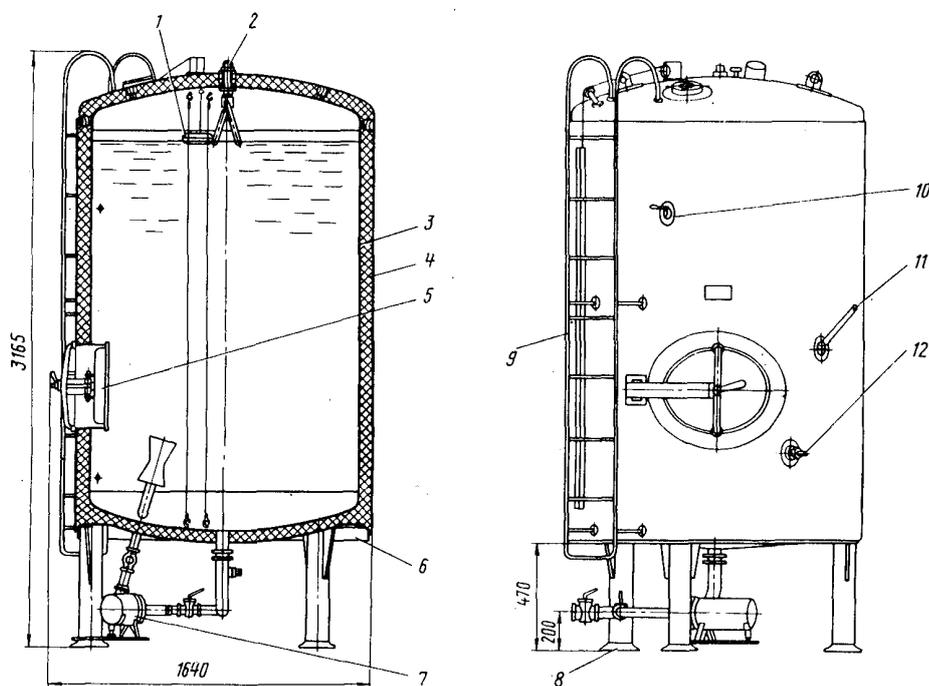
Общий вид резервуара В2-ОМВ-2,5: 1 – указатели уровня молока; 2 – моечное устройство; 3 – корпус; 4 – изоляция; 5 – люк; 6 – основание; 7 – перемешивающее устройство; 8 – опора; 9 – лестница; 10 – кран для отбора проб; 11 – термометр; 12 – манометрический термометр
